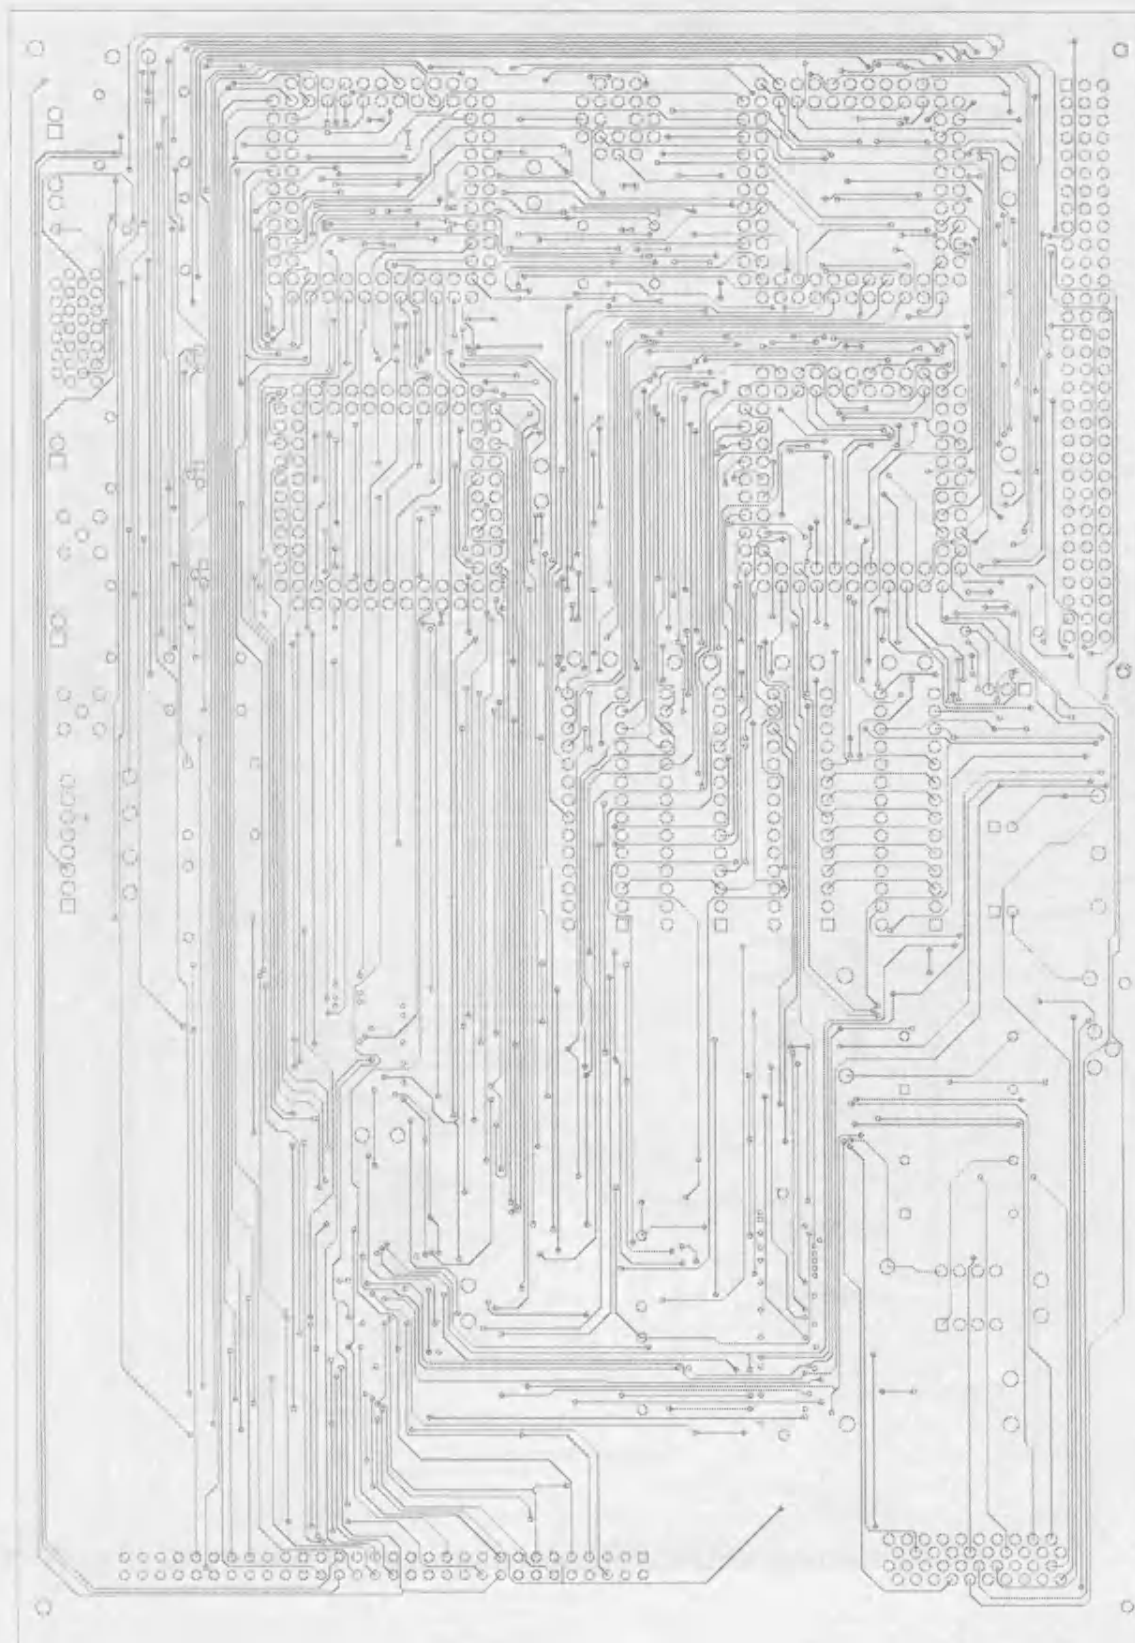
Aspecto del rutado de pistas por la cara de soldaduras de la tarjeta interface S-LINK.
